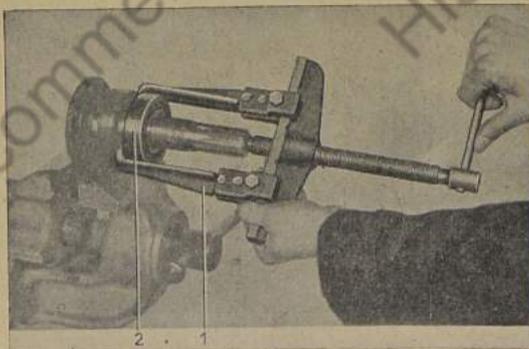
Hochschulterkugellager von Flanschswelle abziehen
